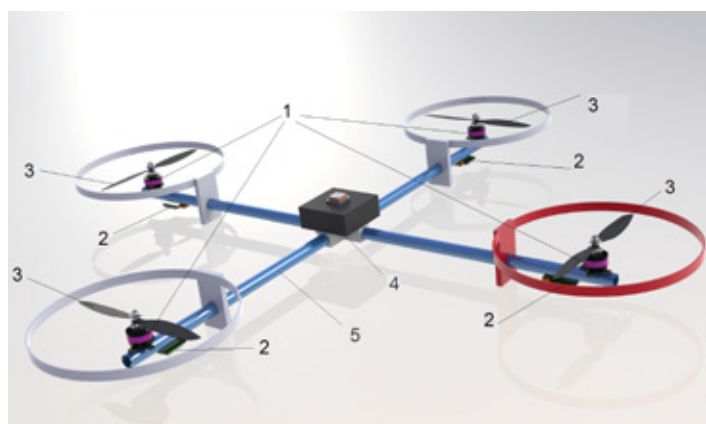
Общий вид квадрокоптера: 1 – бесколлекторные двигатели; 2 – регуляторы оборотов; 3 – винты 10x45 разнонаправленного вращения; 4 – центральная плата управления; 5 – фюзеляж (корпус)
